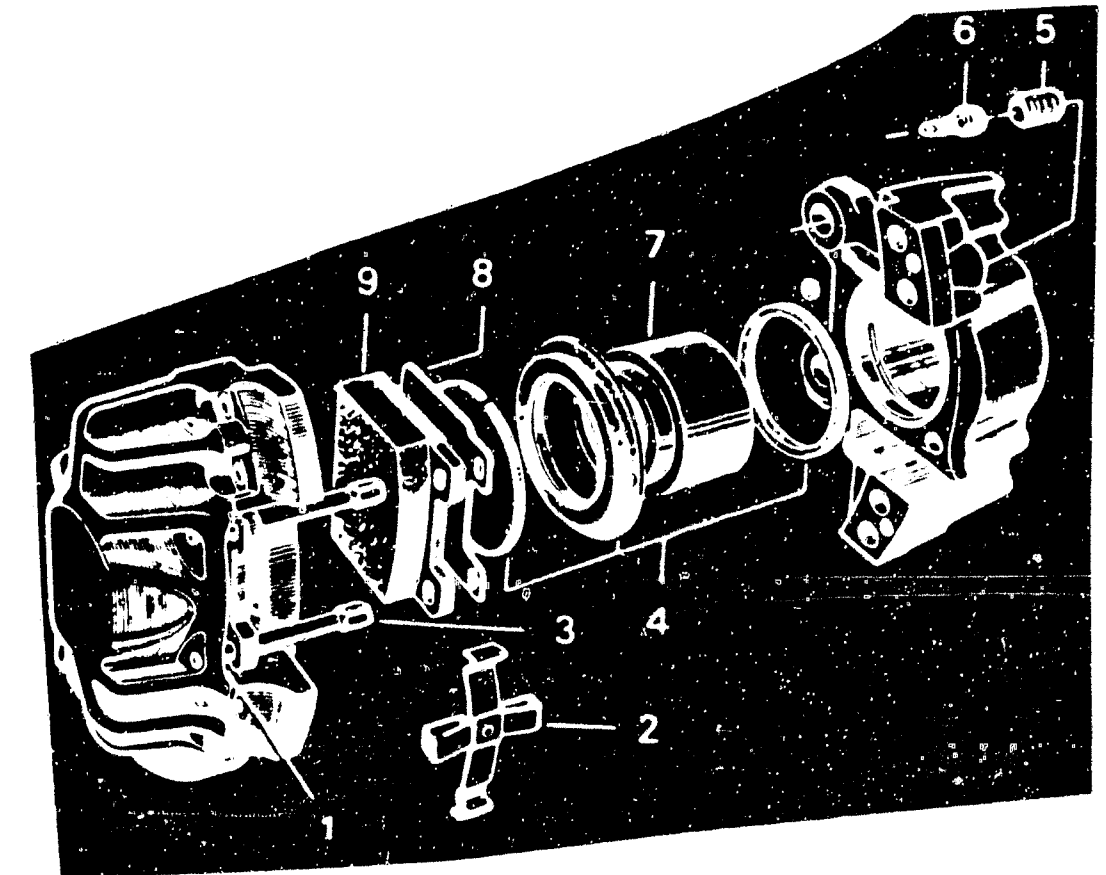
Bremssattel hinten: 1 Bremsgehäuse – 2 Haltefeder – 3 Haltebolzen – 4 Dichtungssatz – 5 Schutzklappe – 6 Entlüftungsschraube – 7 Kolben – 8 Verdrehsicherung – 9 Bremsklötz.
